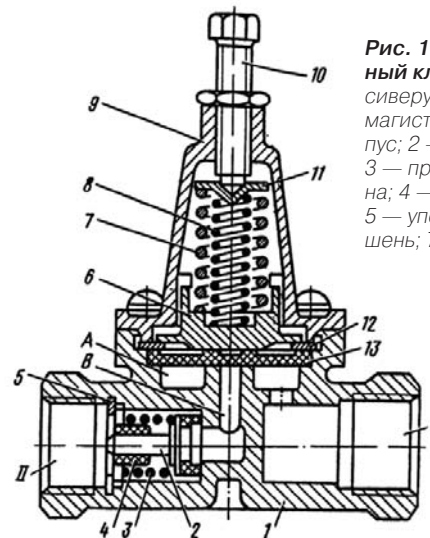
Одинарный защитный клапан: 1 — вывод к ресиверу; 2 — вывод в питающую магистраль прицепа; 3 — корпус; 4 — обратный клапан; 5 — пружина обратного клапана; 6 — направляющая втулка; 7 — упорное кольцо; 8 — поршень; 9, 8 — пружины поршня; 10 — регулировочный винт; 11 — тарелка пружины поршня; 12 — шайба; 13 — диафрагма
